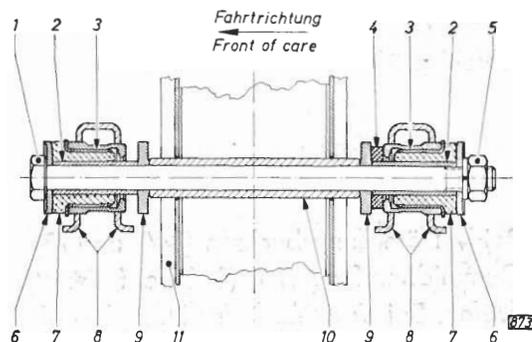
Anordnung – Befestigung oberer Lenker an Stützträger
